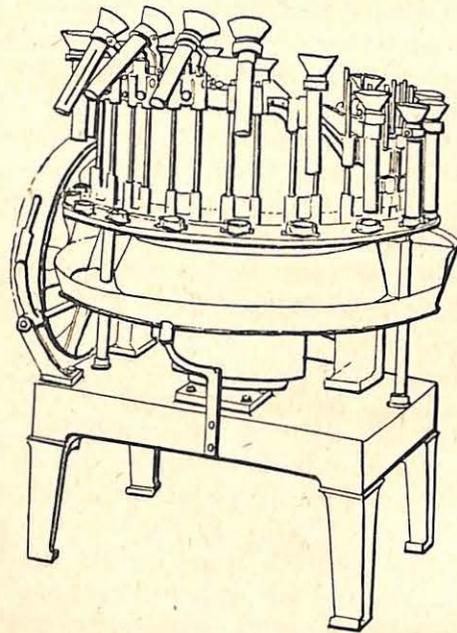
Gaine pulvérulente, machine à gainer type revolver fabrication belge.
